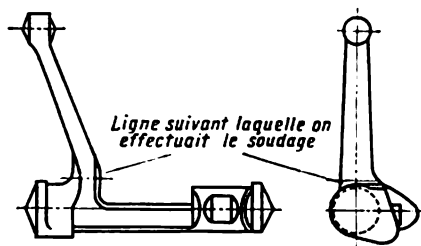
Exemple de remplacement avantageux d'une construction soudée par une pièce estampée
